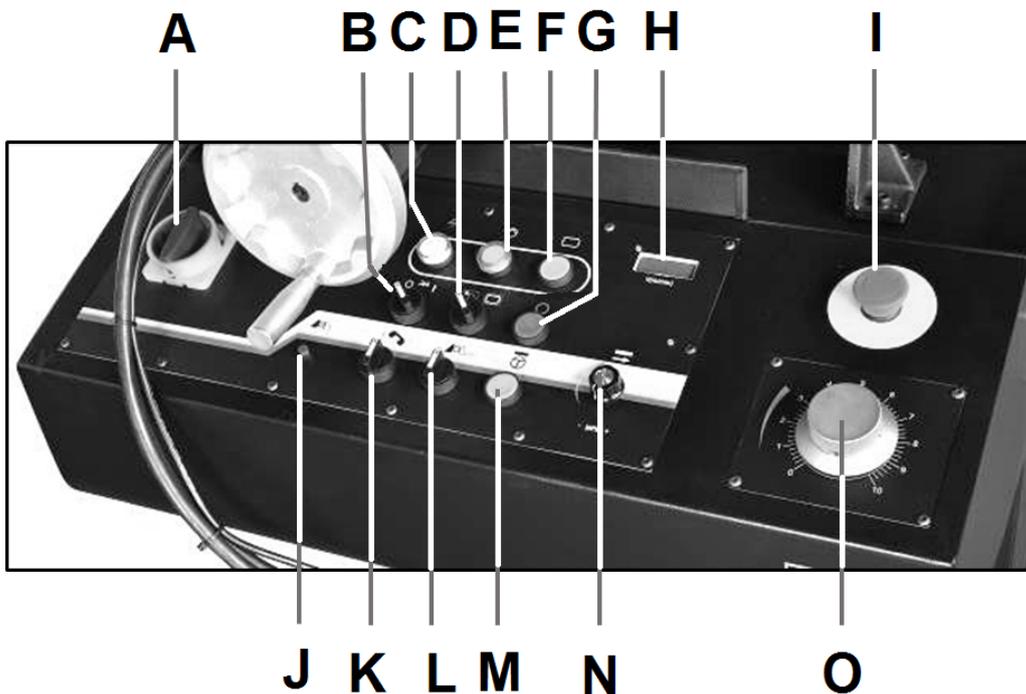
Bezeichnungen der Bedienelemente der Maschine
